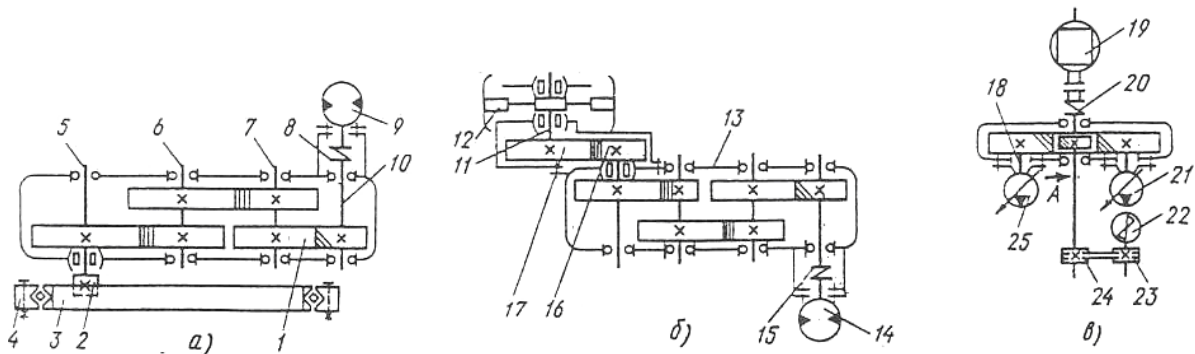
Кинематическая схема привода: а – механизма поворота платформы; б – механизма передвижения; в – насосов силовой установки
